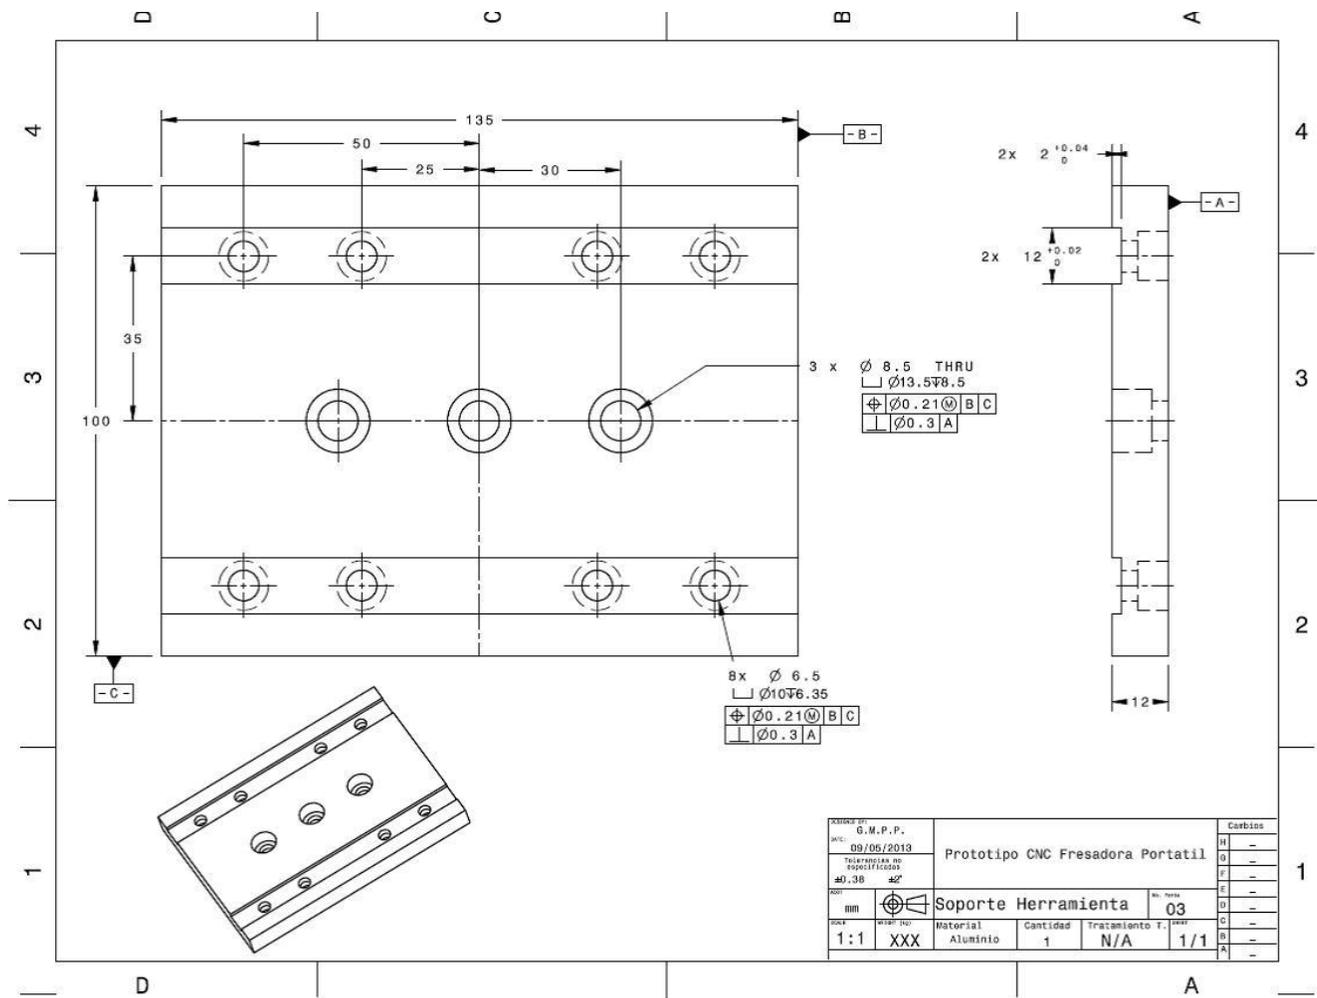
Plano con sistema GD&T soporte eje z
